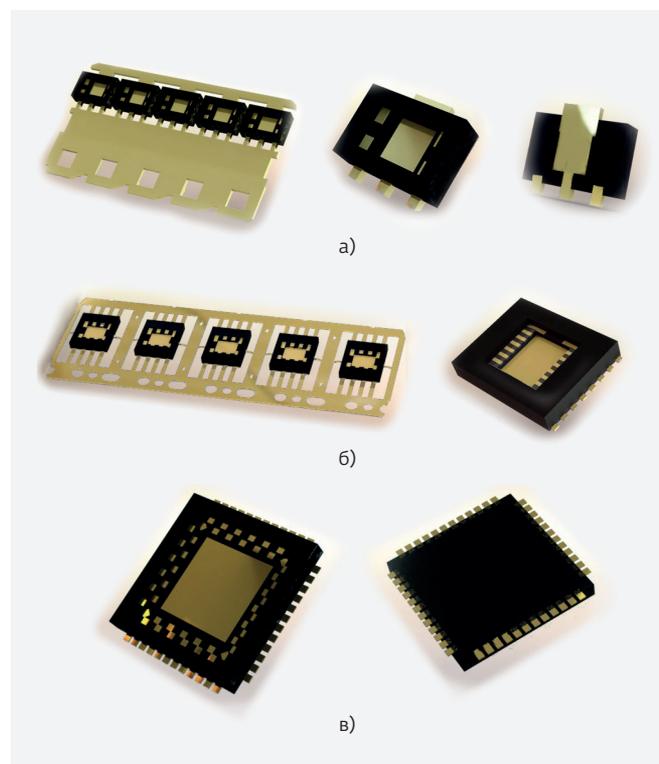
Корпуса, разработанные в ЗАО "Группа кремний ЭЛ": а) тип SOT-89; б) тип SOC-8; в) 48-выводной корпус
